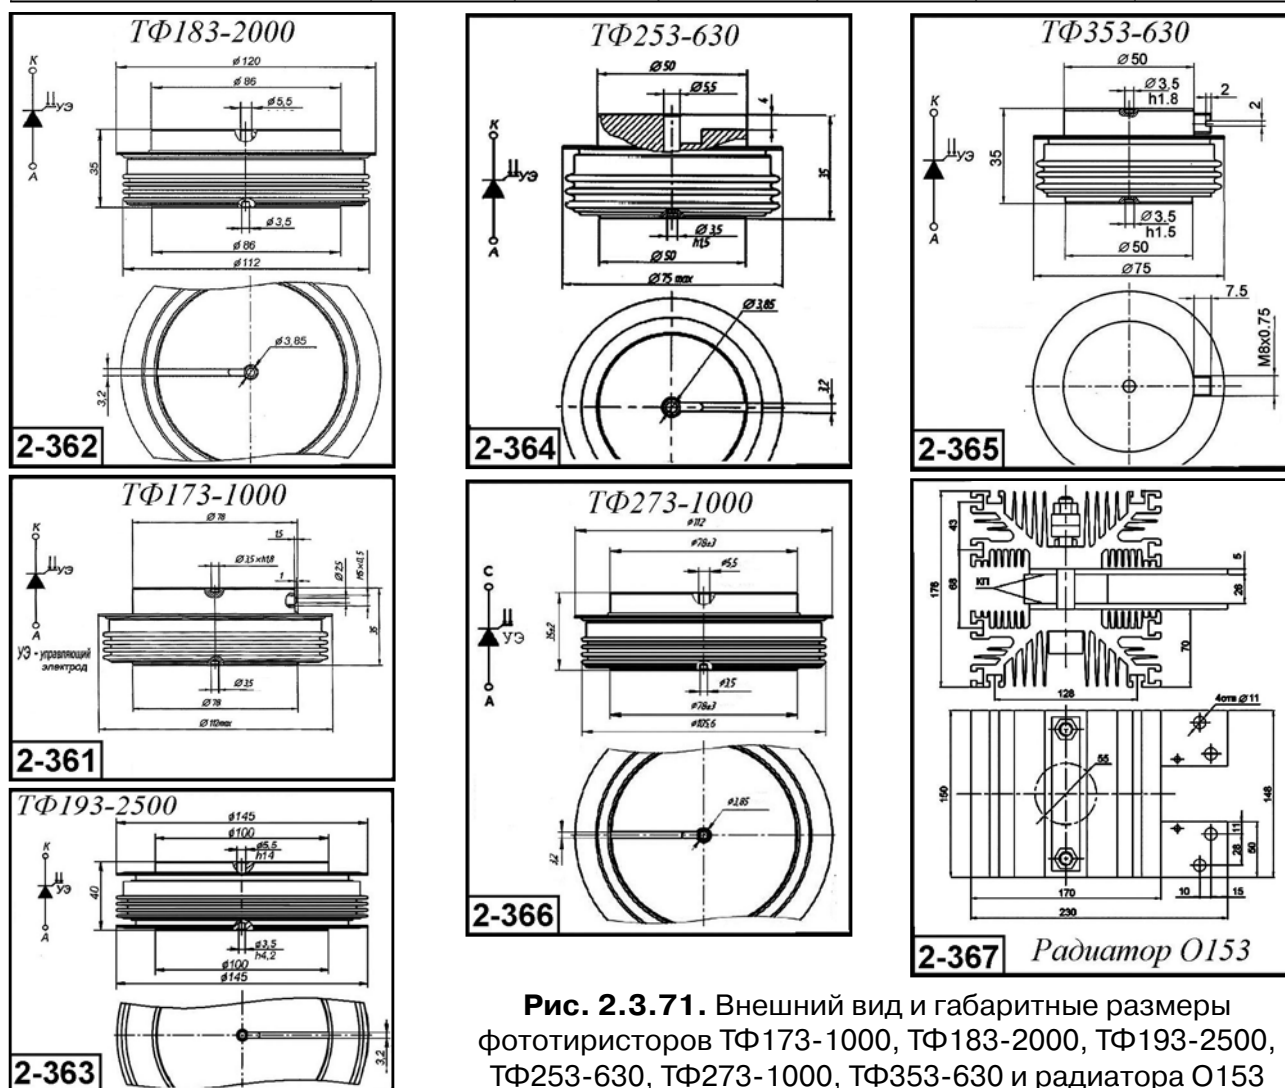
Внешний вид и габаритные размеры фотоthyristоров ТФ173-1000, ТФ183-2000, ТФ193-2500, ТФ253-630, ТФ273-1000, ТФ353-630 и радиатора O153
